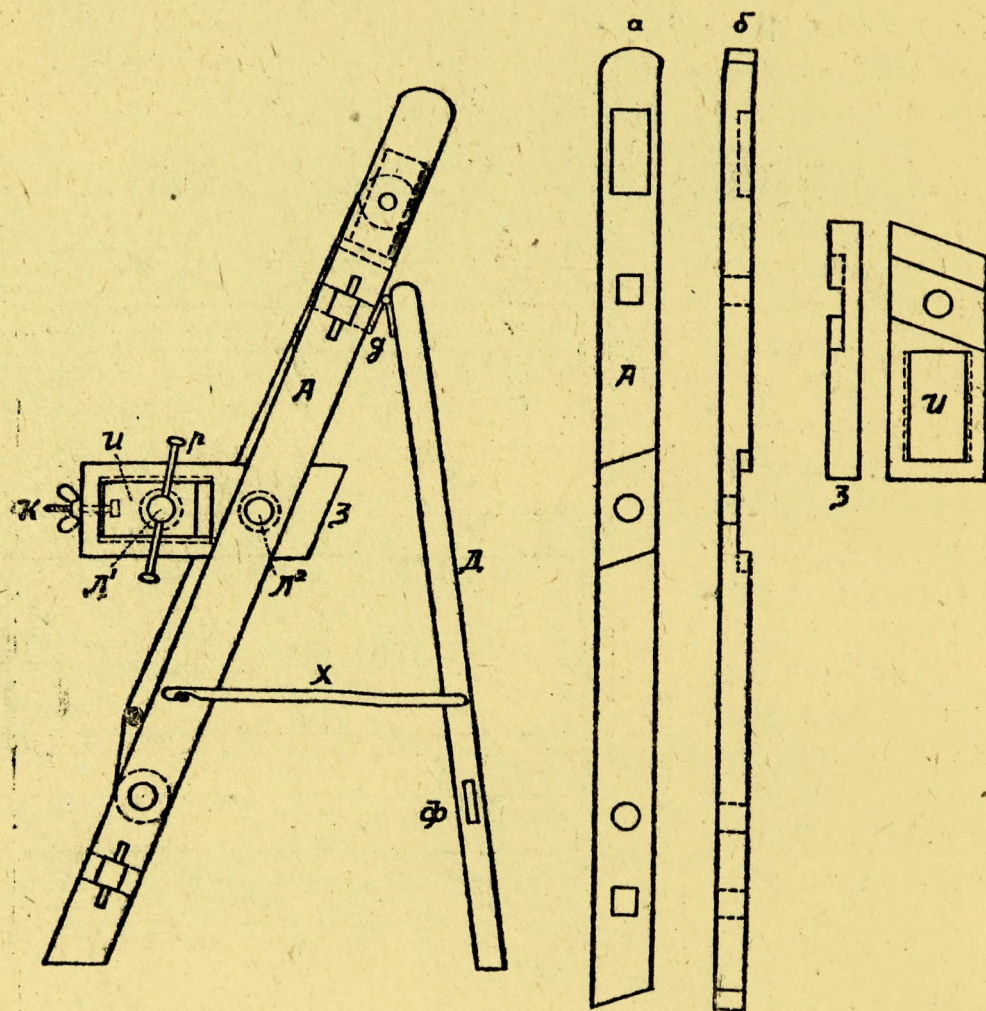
Ковровый станок для круглой основы — вид сбоку.
